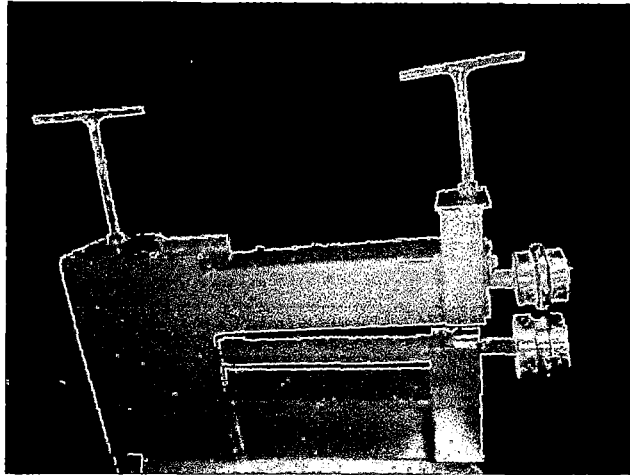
Vista de perfil con los dados hembra-macho en la perfiladora de planchas
